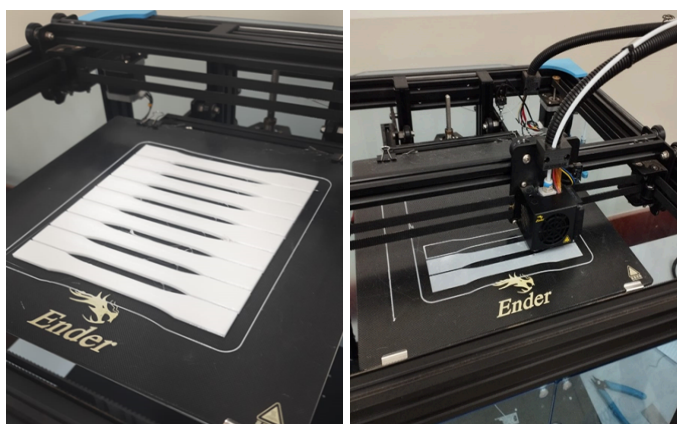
A) Mesa de impressão e corpos de prova durante a impressão. B) Corpos de prova após a impressão finalizada.
